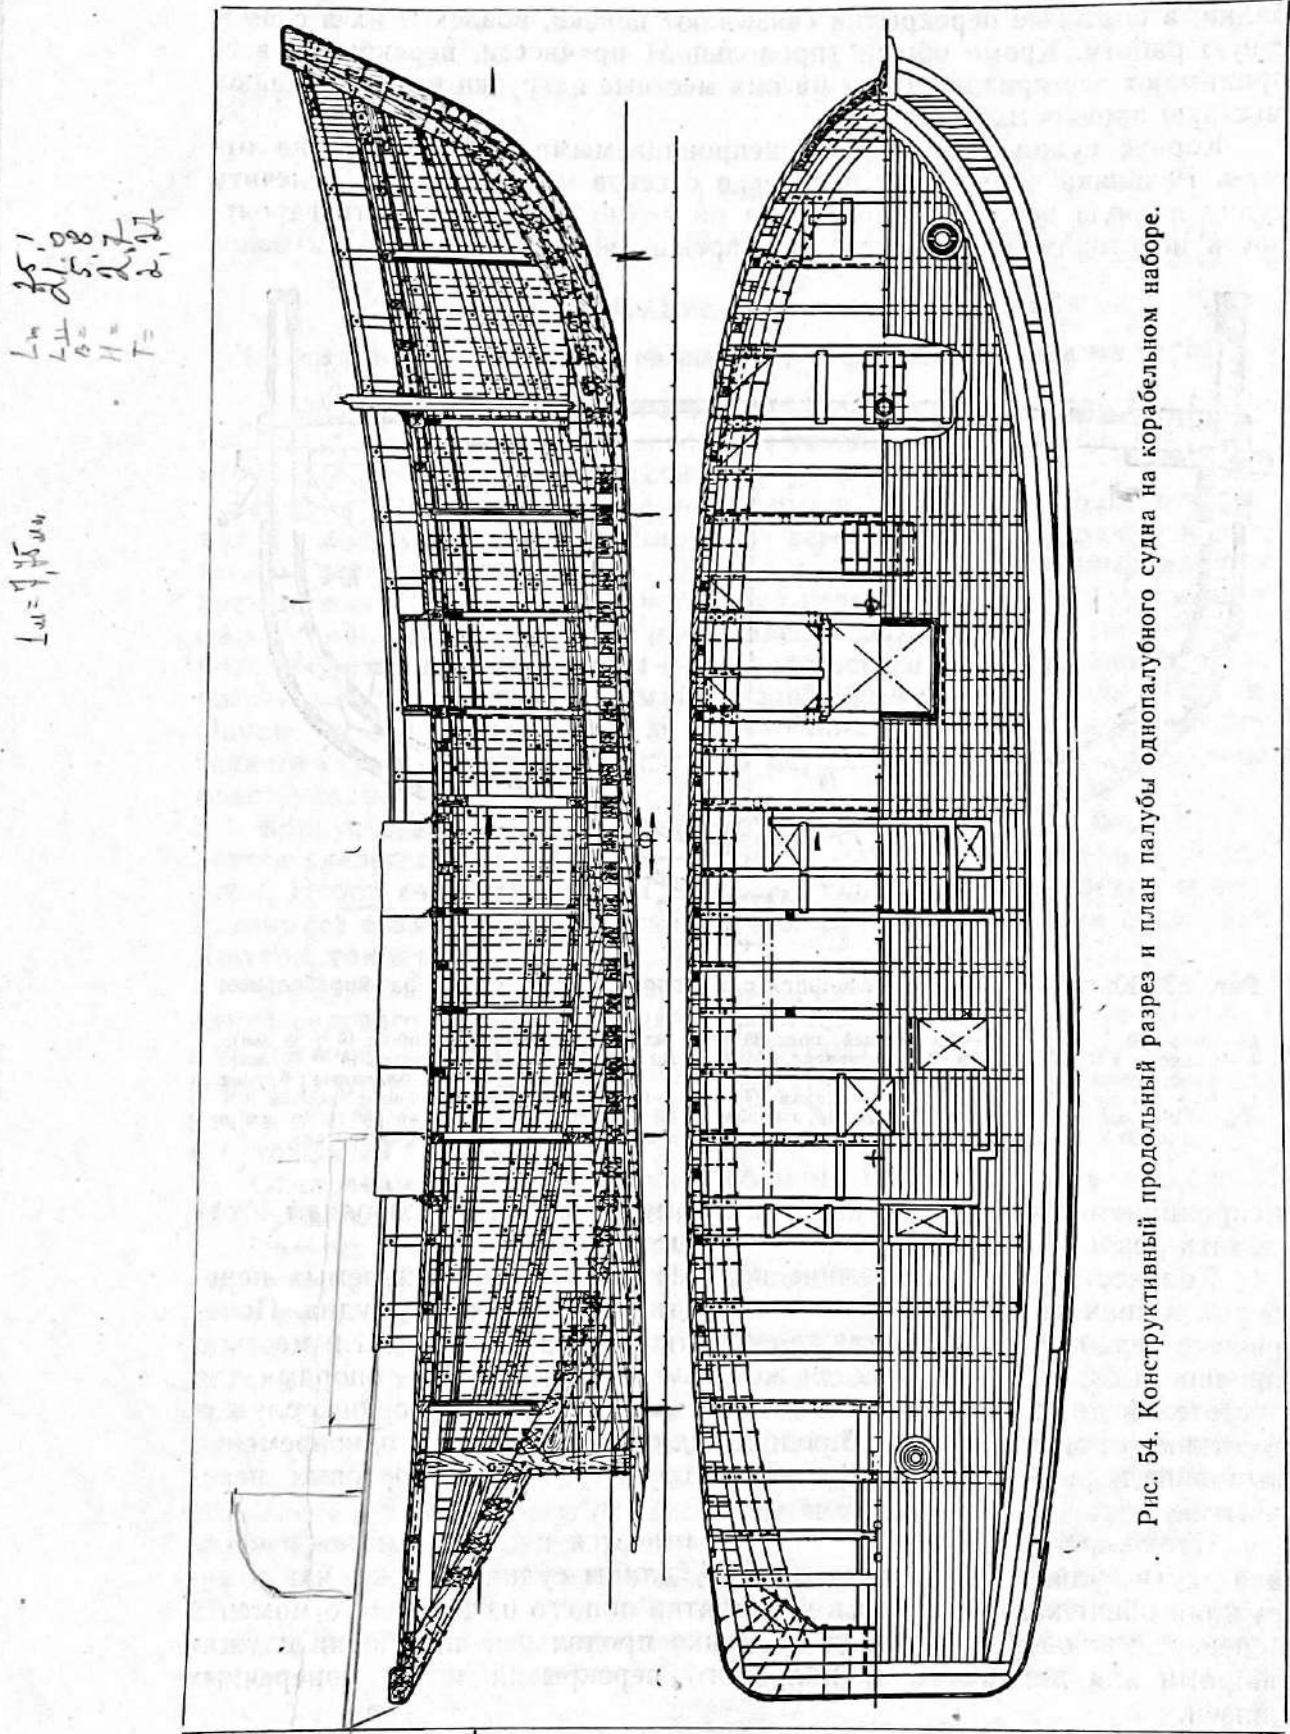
Конструктивный продольный разрез и план палубы однопалубного судна на корабельном наборе.
